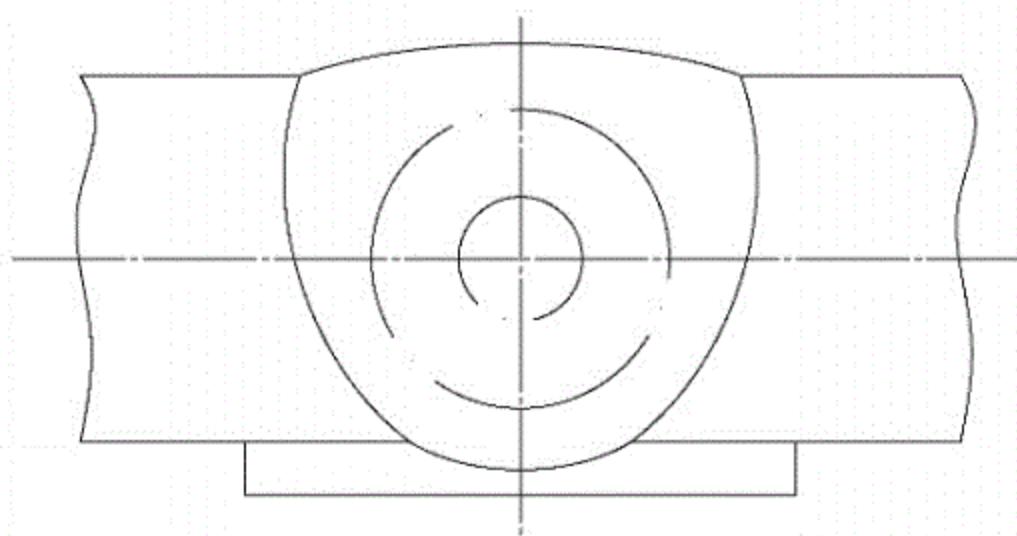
焊接接头圆形带肩拉伸试样
